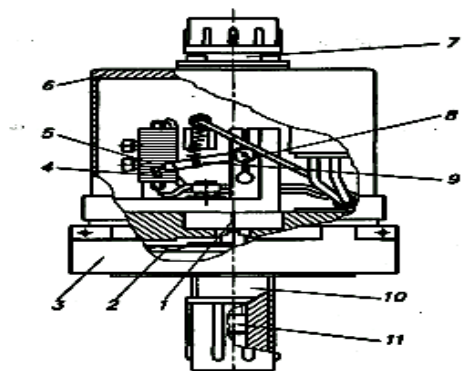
Потенциметрический датчик давления: 1 – лента; 2 – мембрана; 3 – корпус; 4 – контакты; 5 – реостат; 6, 7 – корпус; 8 – ось; 9 – переключатель; 10 – заливка датчика; 11 – гайка
